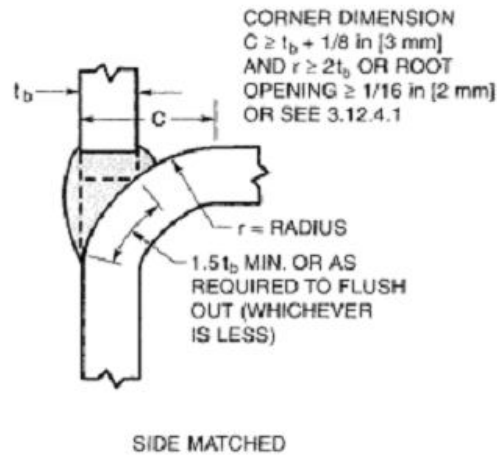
Tipo de soldadura típica en las conexiones
